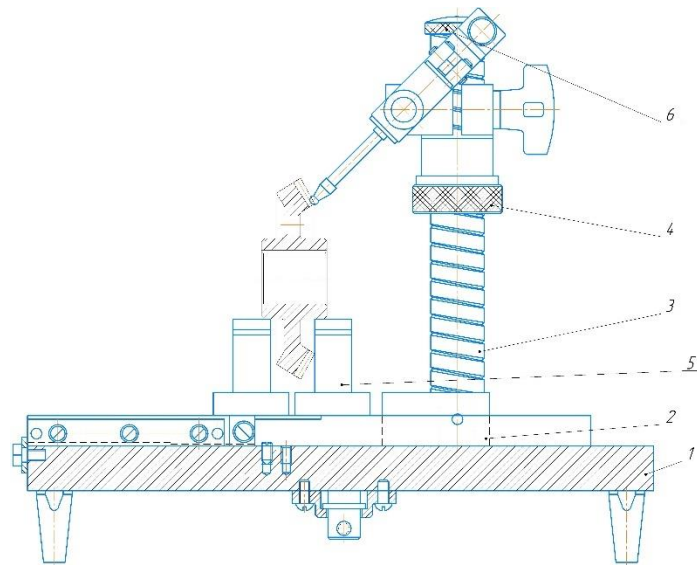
Схема контрольного пристосування для вимірювання профілю зубців
